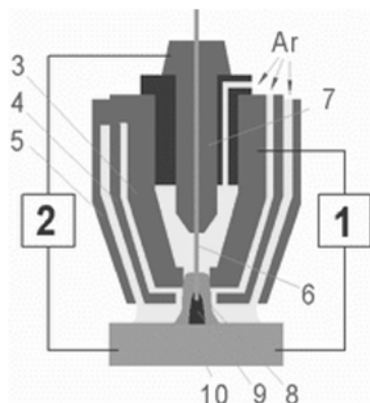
Плазмотрон для сварки плавящимся электродом:
